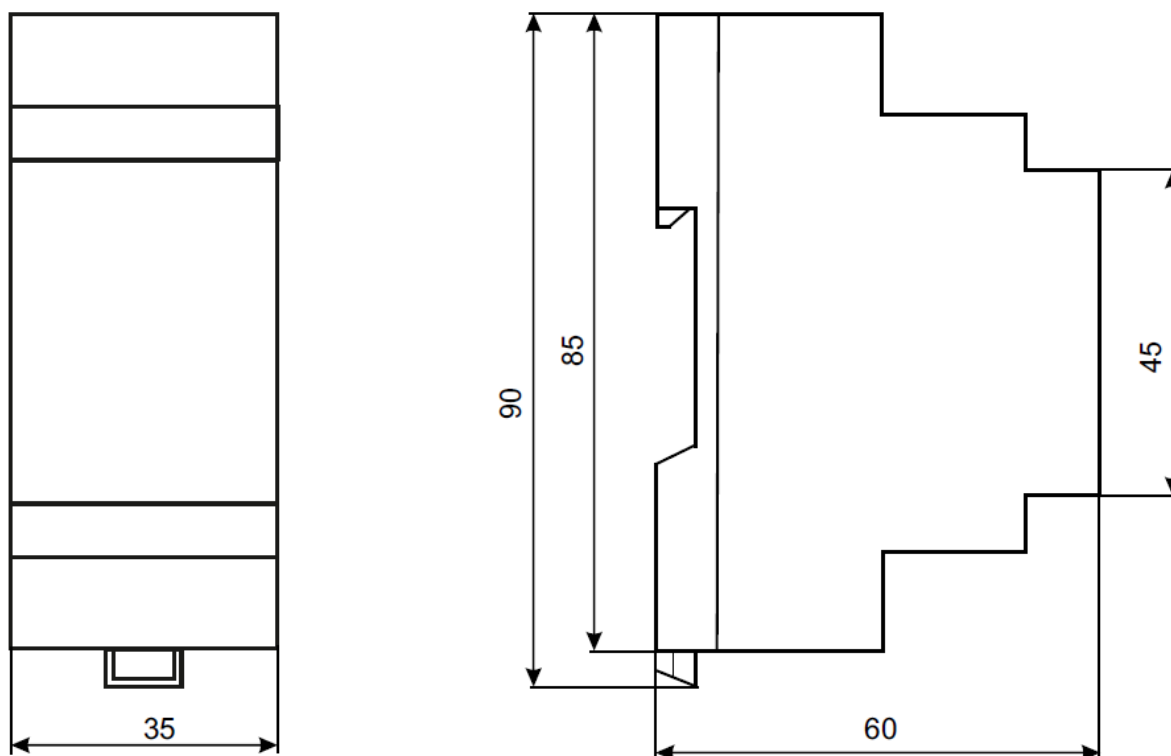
Габаритные размеры преобразователей интерфейсов IC-31С, выполненных в корпусе К-04-03
